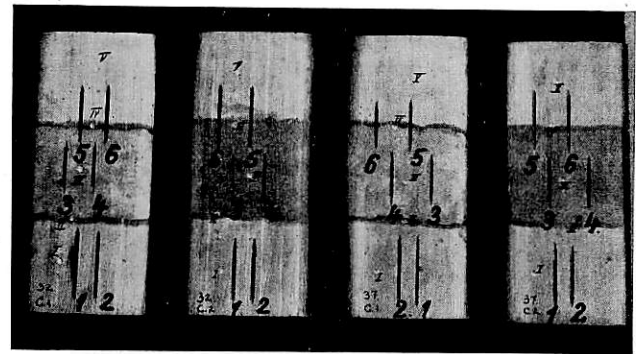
Die Brinell- und Spindelproben des geschweißten Schienenstoßes.
